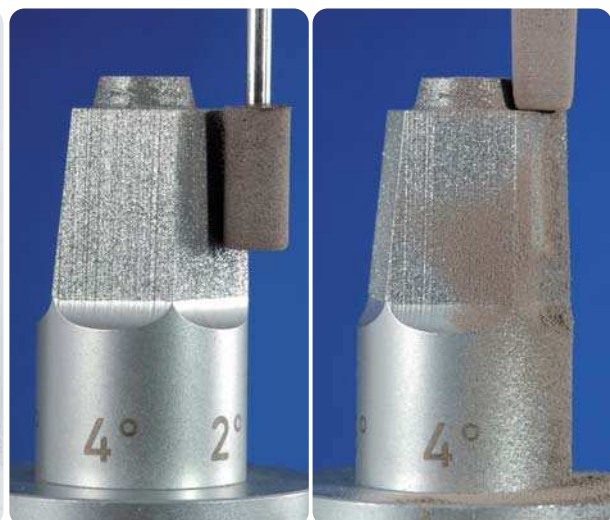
Die Abrichtblöcke für die Teleskop- und Konuskronen-Polierer. – Abb. 18: Abrichten des braunen Vorpolierers auf 2°. – Abb. 19: Abrunden des Polierers für das Bearbeiten der Hohlkehle.
